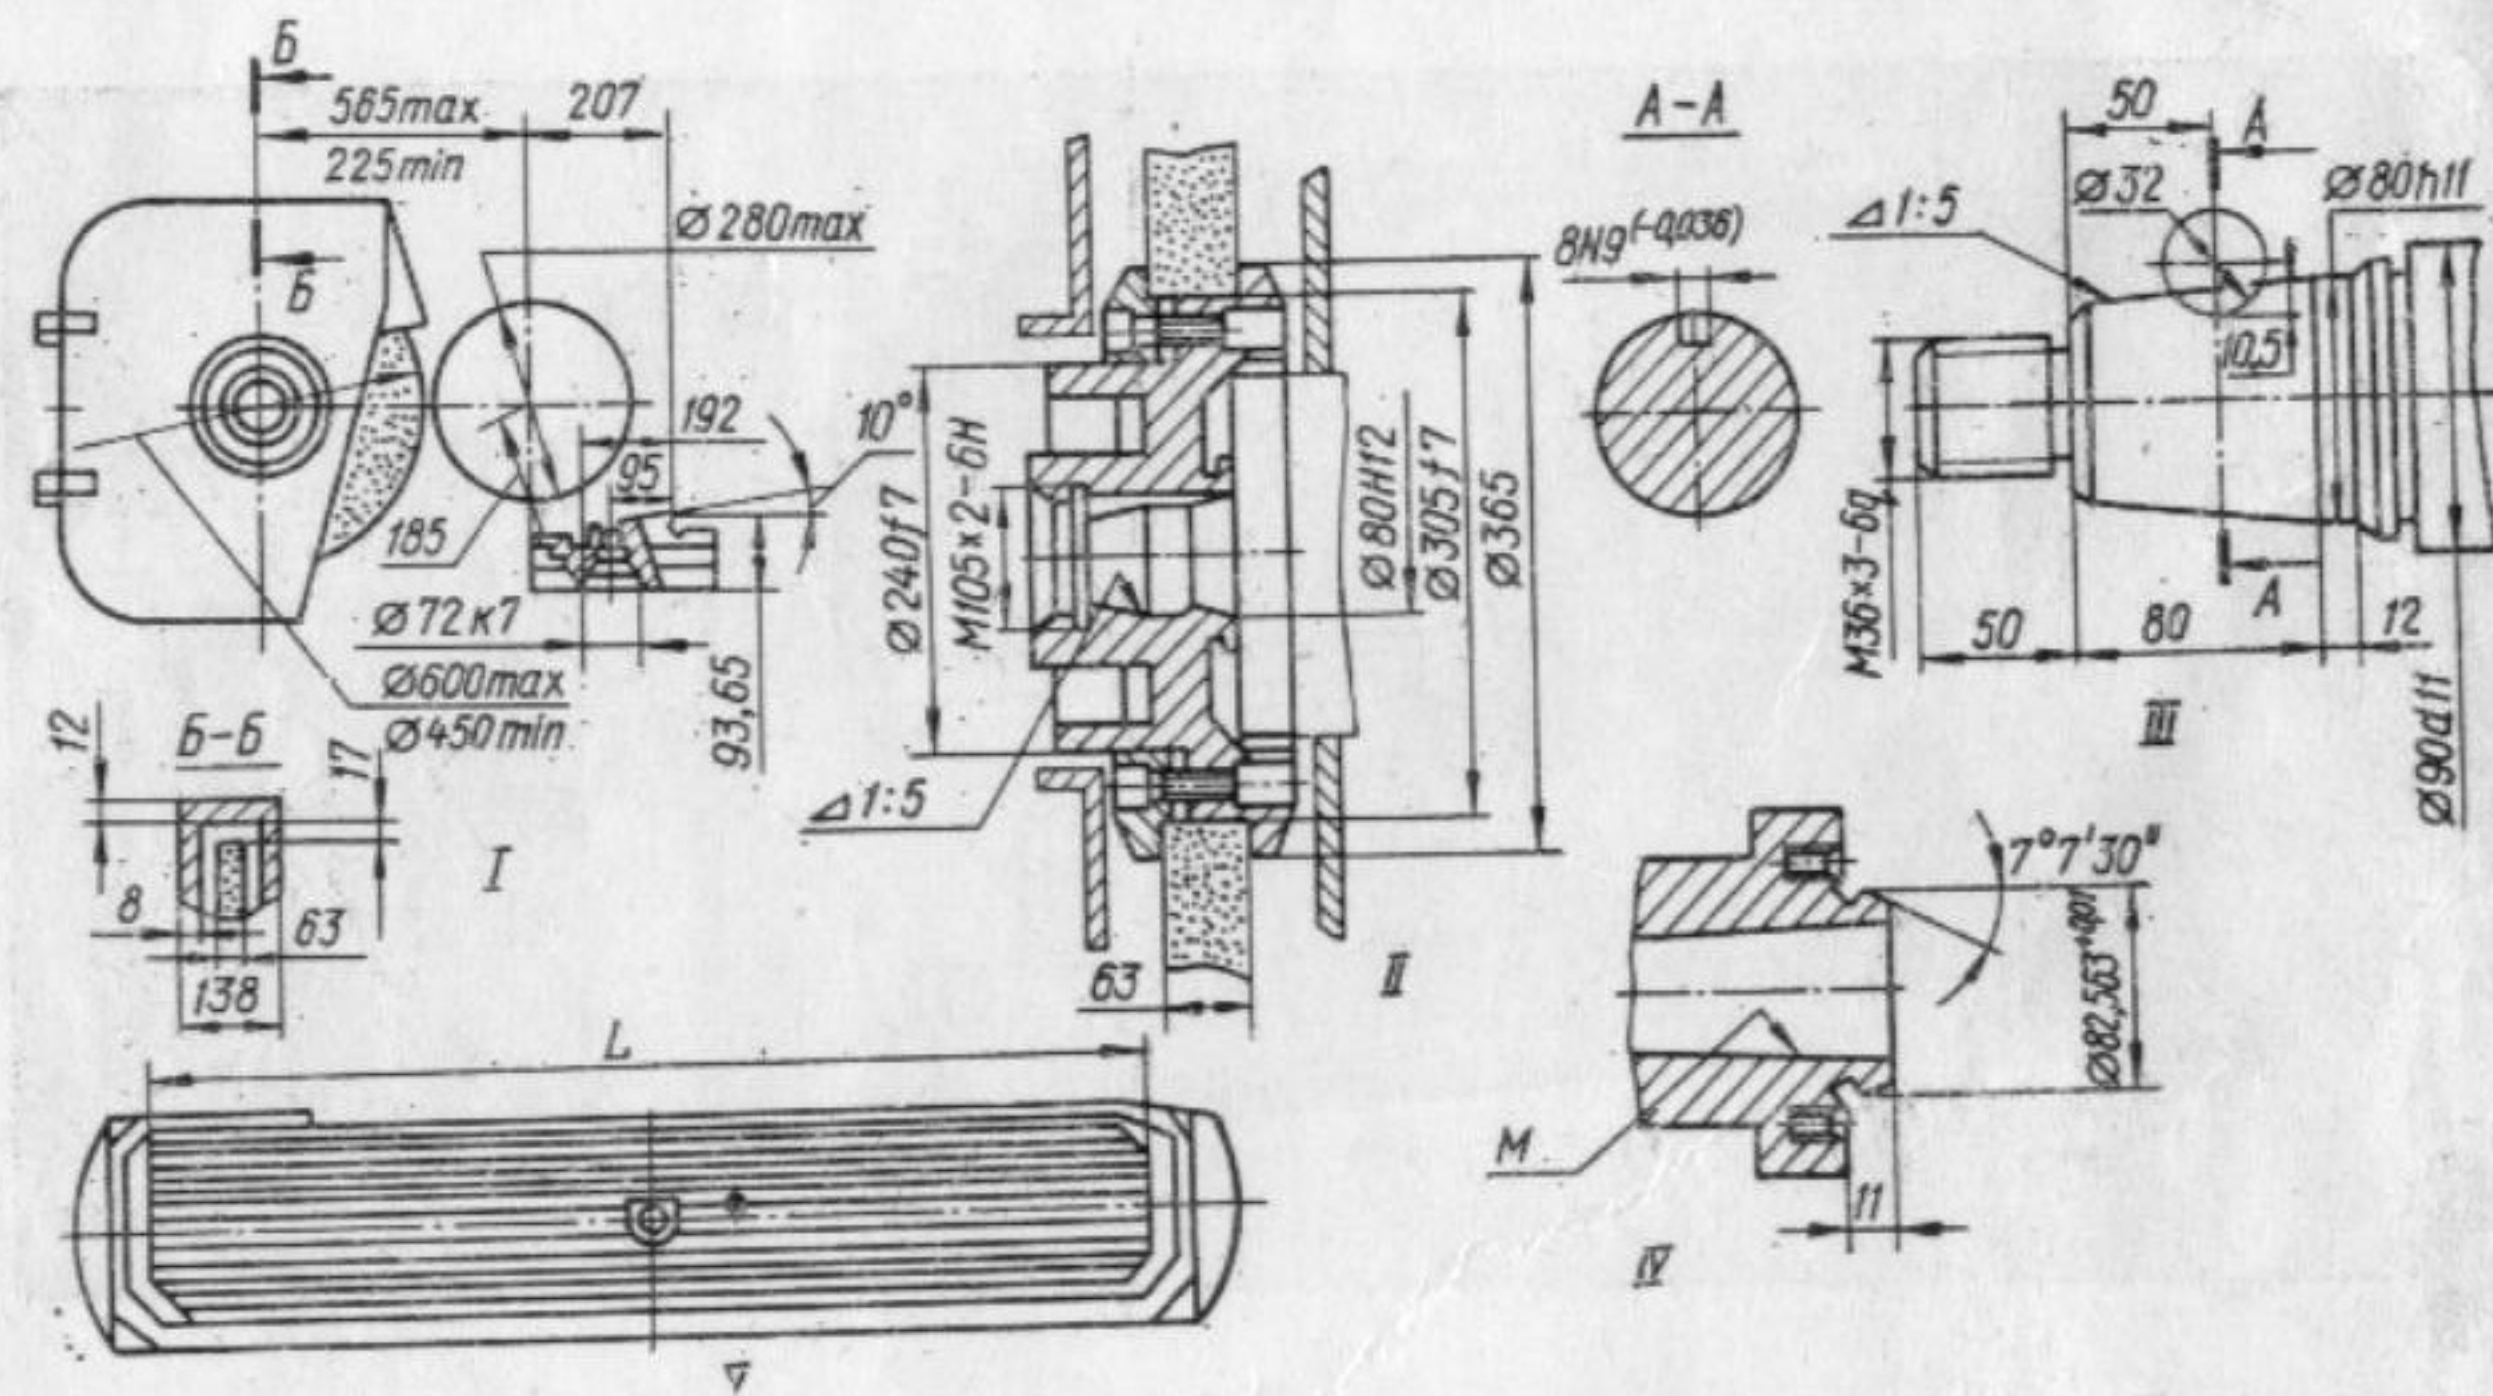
Габариты рабочего пространства, посадочные и присоединительные базы станков ЗУ131ВМ, ЗУ133МВ:
